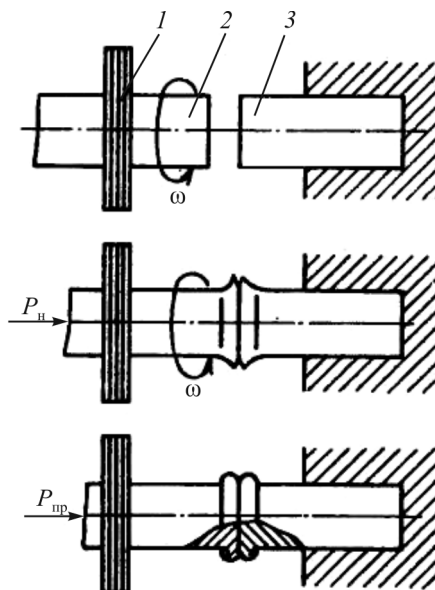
Схема инерционной СТ: 1 – маховик; 2, 3 – свариваемые заготовки
